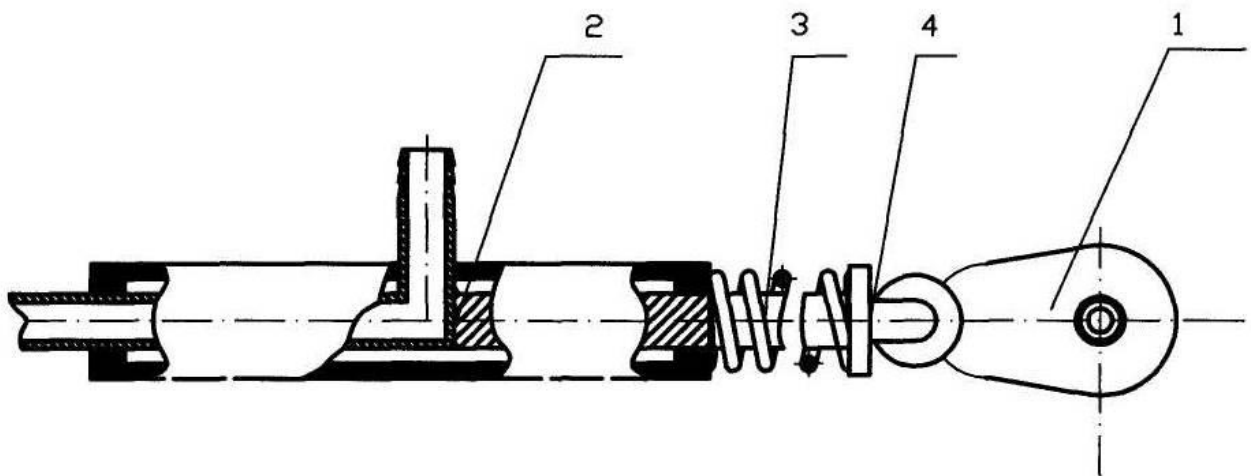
Механізм руху ріжучого вузла: 1 – рушійний механізм; 2 – шток; 3 – пружина; 4 – ролик
